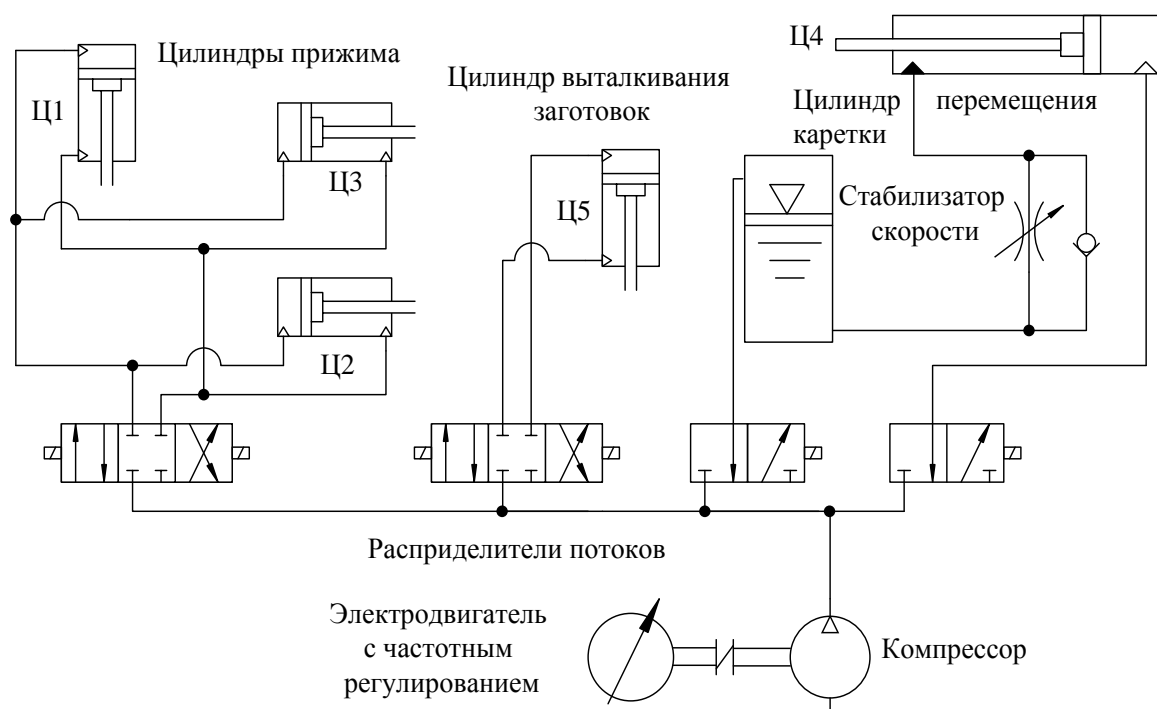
Усовершенственная пневмо-гидравлическая схема шипорезного станка
